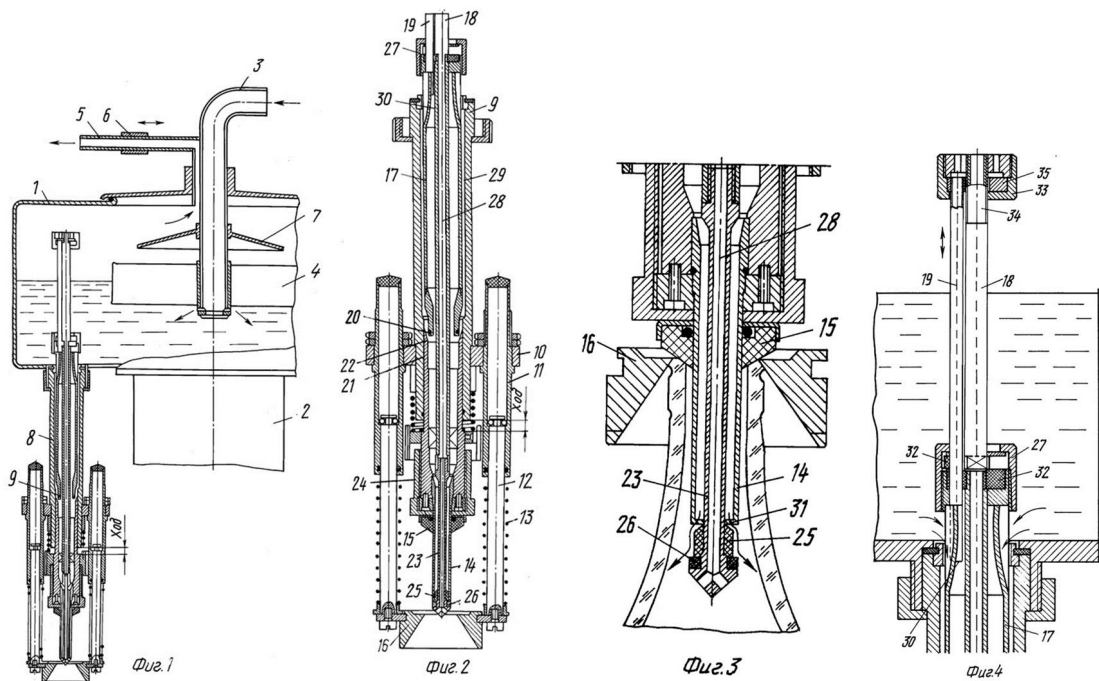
Фігури до патенту: 1 – резервуар з дозатором; 2 – пристрій для дозування рідини; 3 – пристрій для дозування рідини з пляшкою; 4 – верхня частина пристрою для дозування рідини
